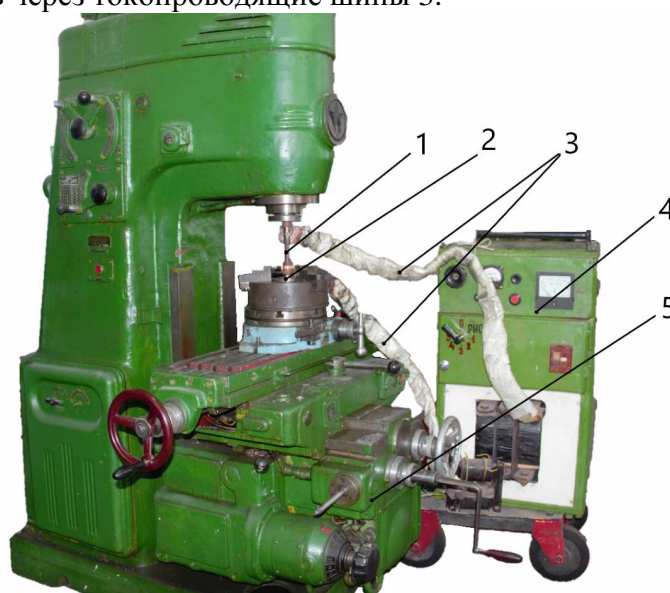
Экспериментальная установка для ЭМЗ рабочих поверхностей шлицев втулки: 1 – инструмент для ЭМЗ; 2 – экспериментальная шлицевая втулка; 3 – токопроводящие шины; 4 – источник питания; 5 – вертикальный консольно-фрезерный станок 6В11
